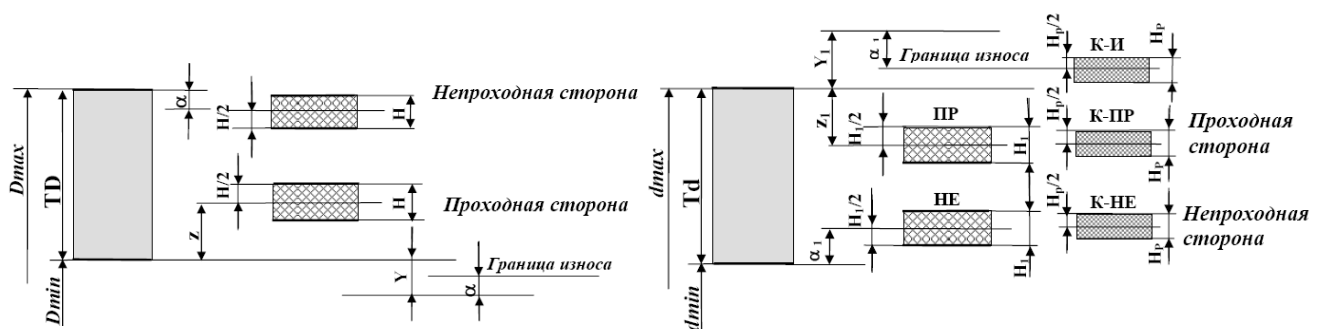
Схемы расположения полей допусков калибров:
